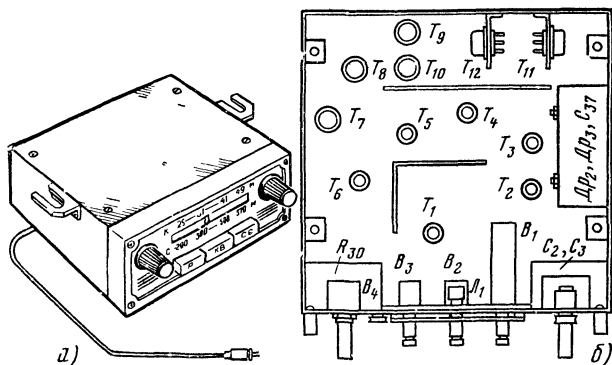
Внешний вид автомобильного приемника (а) и схема размещения деталей в корпусе (б).
